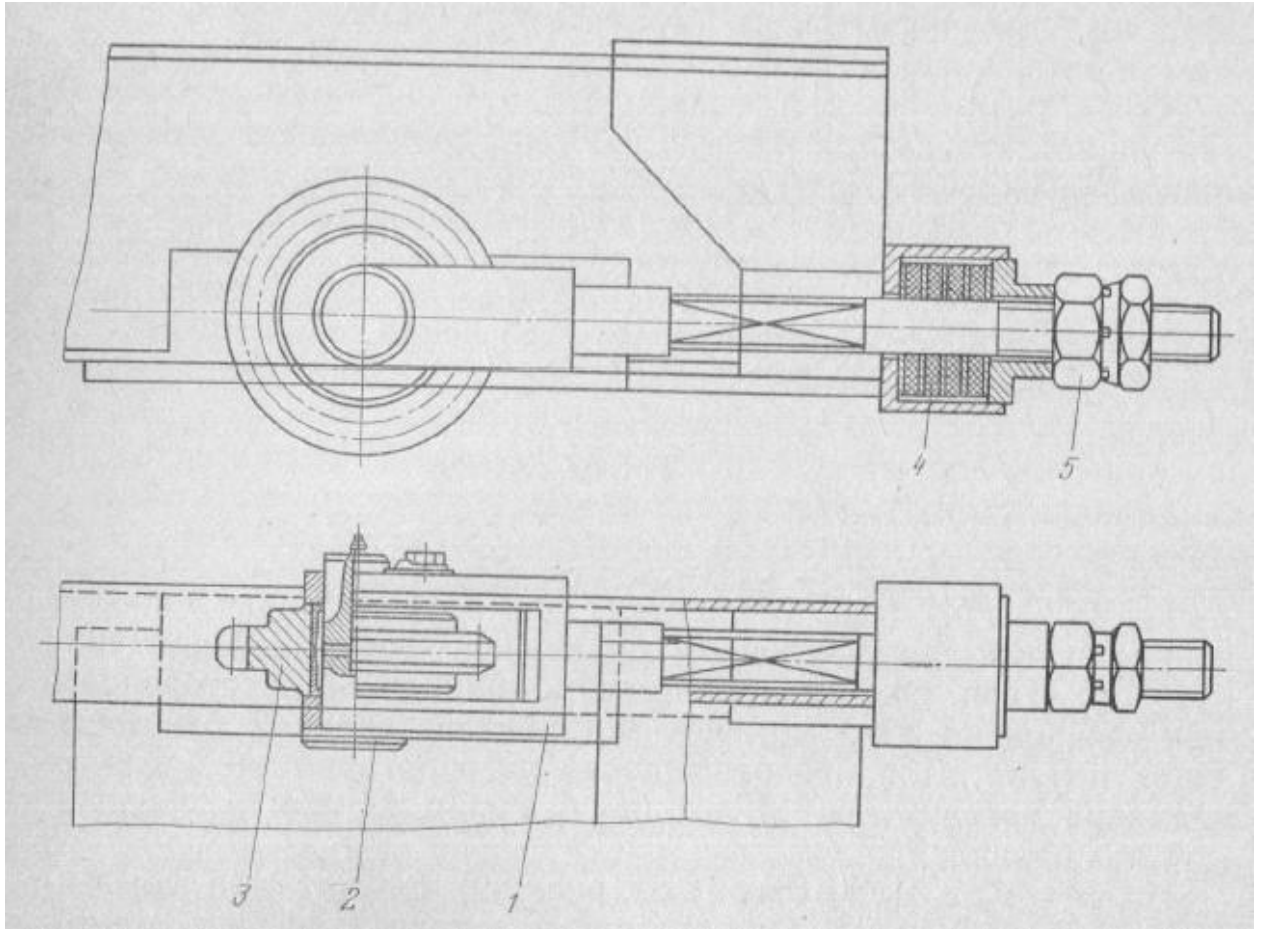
Натяжний пристрій бурового верстату СБУ-125
